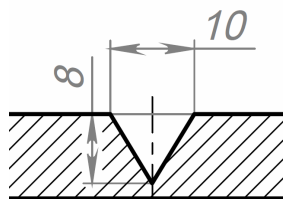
Поперечное сечение канавки шва на свариваемых заготовках
